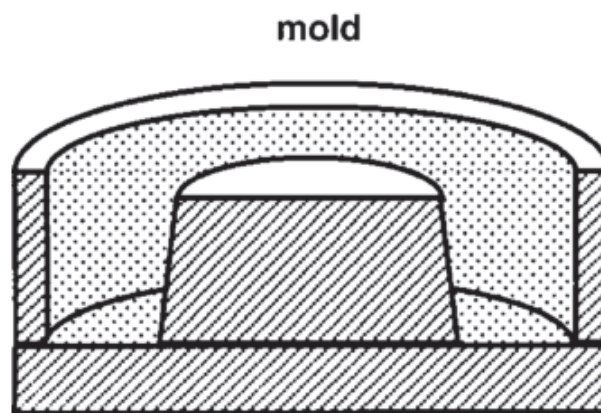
Plan en coupe d'un moule du test de l'anneau [22]
